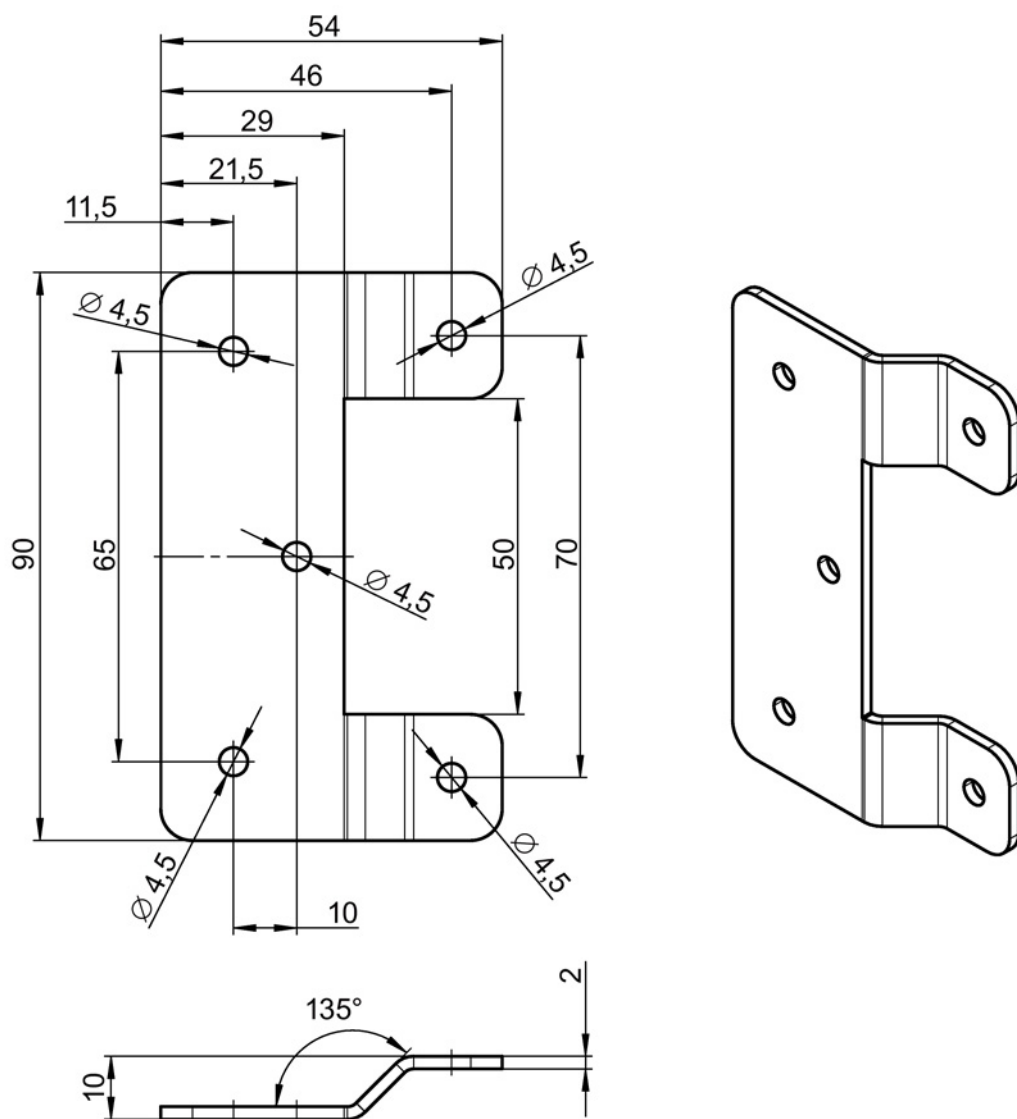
Montage mural X-300EEC (cotes en mm)
